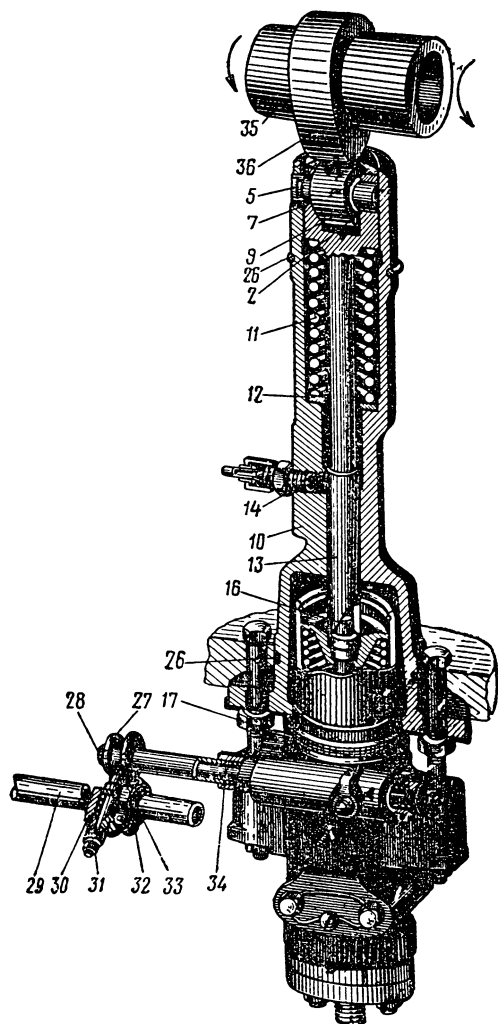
Толкатель в сборе с топливным насосом (обозначения см. на рис. 78):
